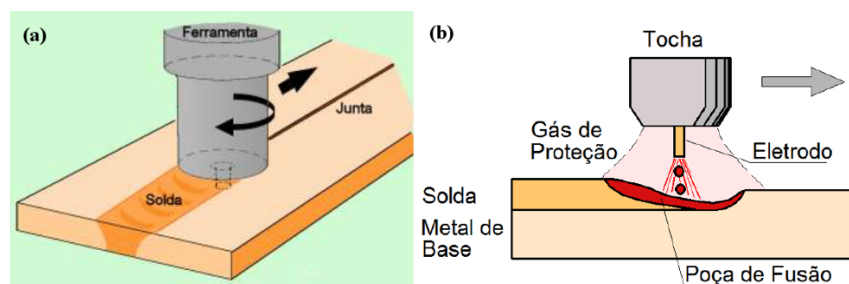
Processos de soldagem: (a) Soldagem por fricção com mistura (FSW), (b) soldagem GMAW. (Adaptado de Modenesi et al., 2012).
